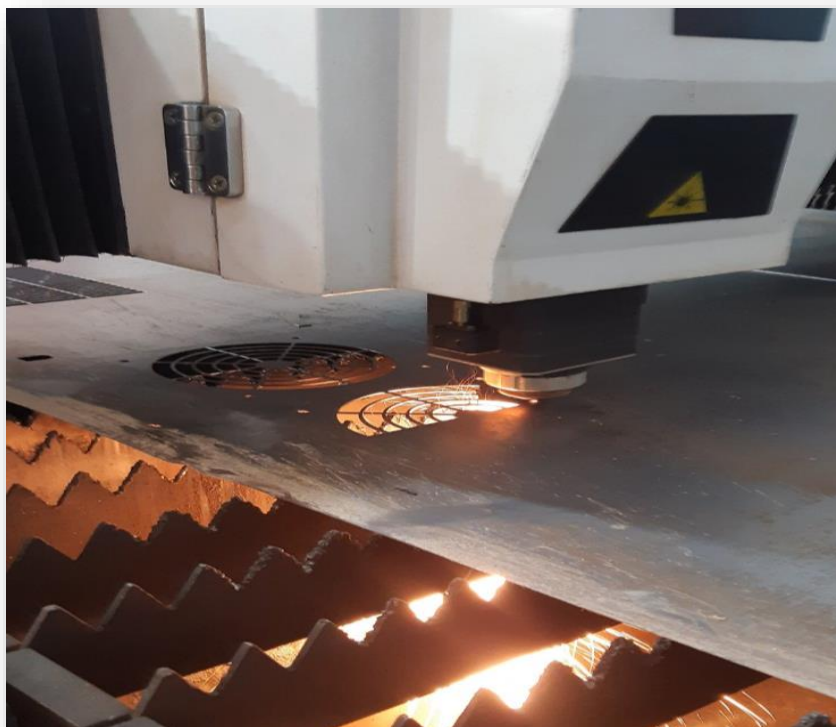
La découpe au laser sur la feuille de tôle de 1mm.
